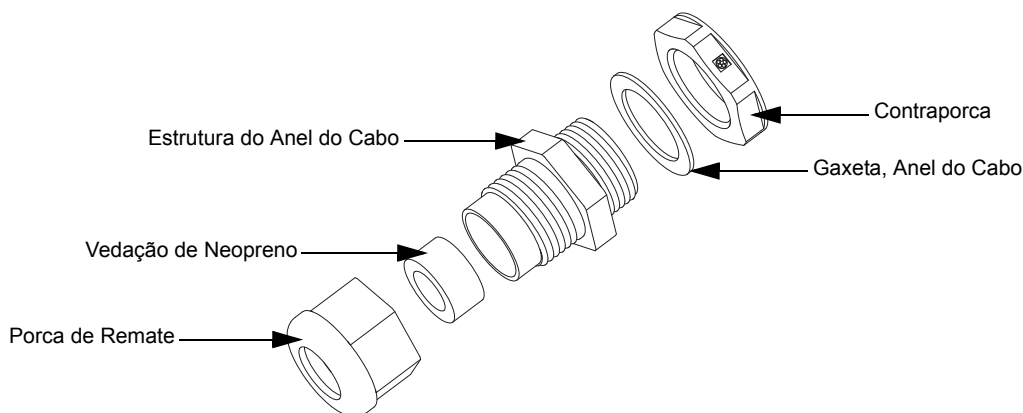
Conjunto de Anéis do Cabo com Gaxeta
